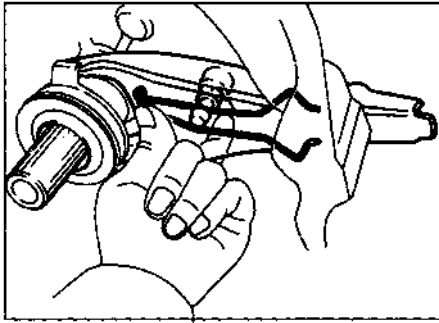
Отстегните вилку сцепления от шаровой опоры с задней стороны рычага
